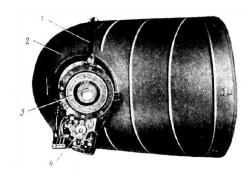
Двигатель ТВ2-117A (вид на правый двигатель сзади):
